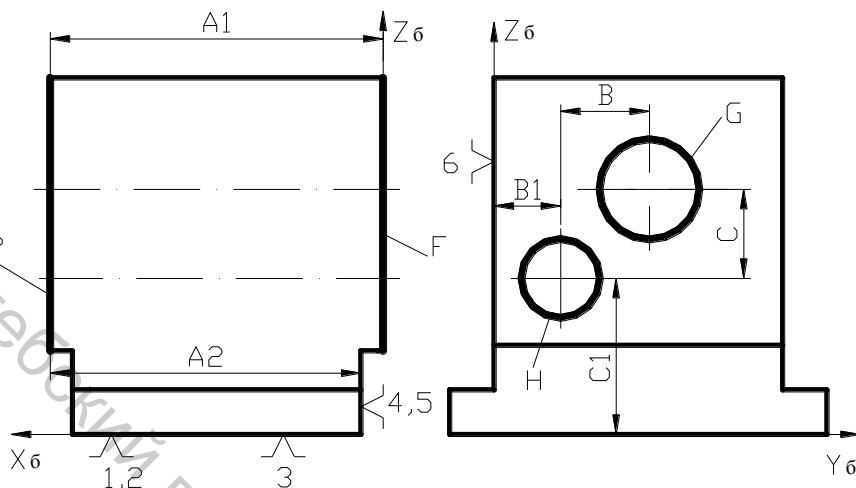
Настроечные базы при обработке заготовки на станке с ЧПУ, оснащённом поворотным столом
